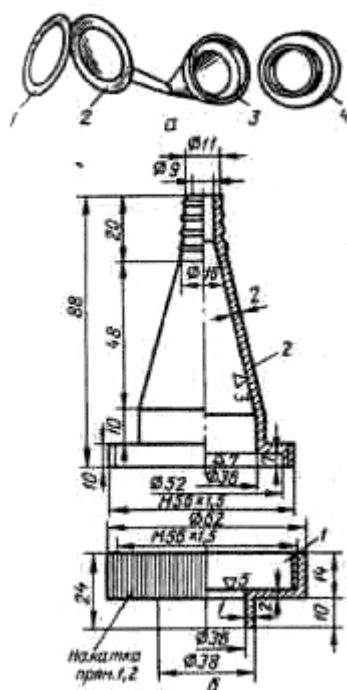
Устройство фильтра и патрона: а — фильтр АФА-ВП: 1 — защитное бумажное кольцо; 2 — фильтр; 3 — корпус конусного патрона; 4 — зажимная гайка; б — патрон к фильтру АФА-ВП-10: 1 — зажимная гайка; 2 — корпус патрона.
